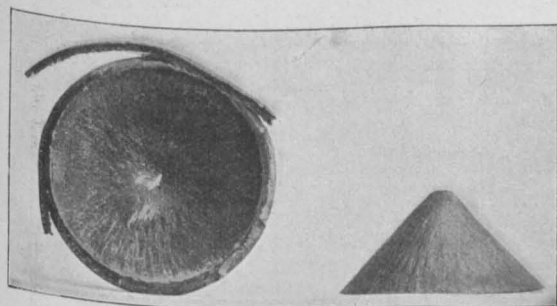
Stauchprobe aus Messing; Druckkegel und nicht gesprengtes Ringstück.
